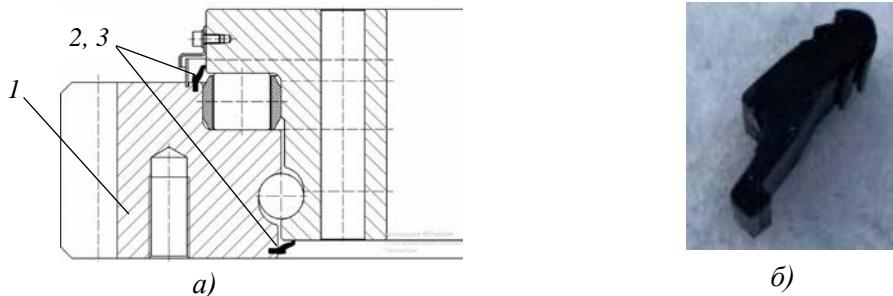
Опорно-поворотный круг: а – элемент опорно-поворотного устройства; б – уплотнитель
